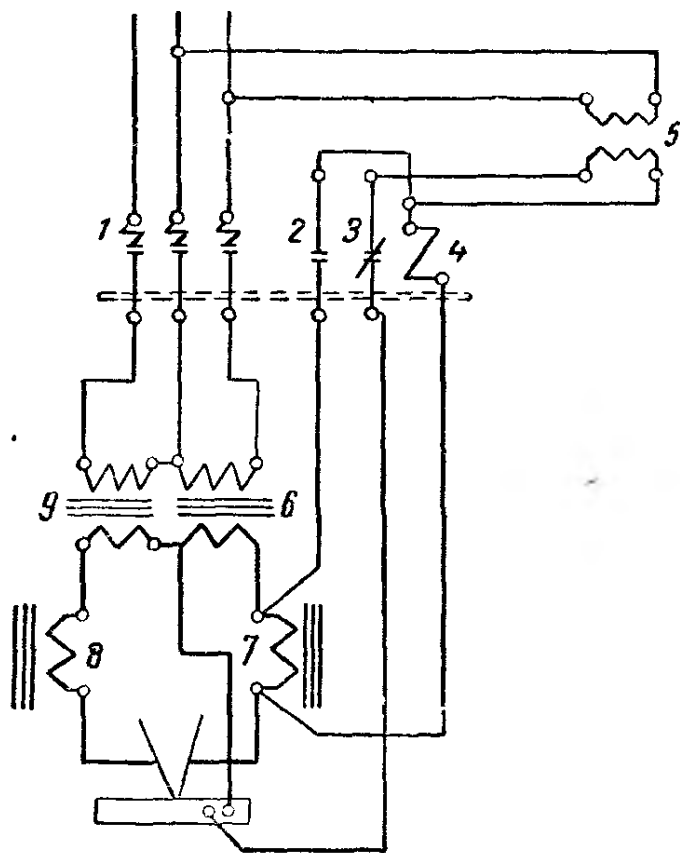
Схема включения двух однофазных трансформаторов при сварке трехфазной дугой:
